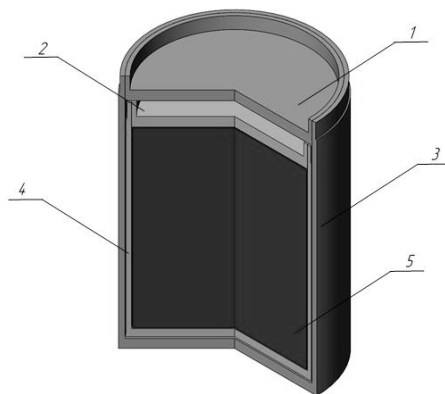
Общий вид источника типа ГИК: 1 – крышка наружной капсулы, 2 – крышка внутренней капсулы, 3 – корпус наружной капсулы, 4 – корпус внутренней капсулы, 5 – заготовка кобальта
